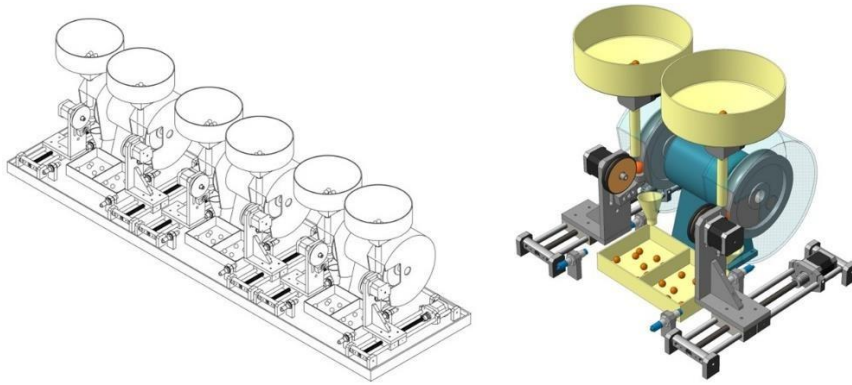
Компоновка багатопозиційного верстата-автомата паралельної дії:
